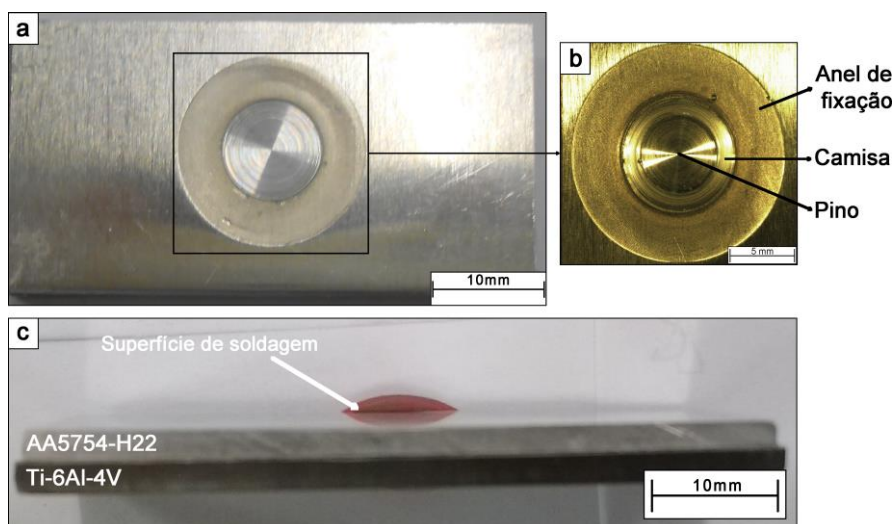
Junta AA5754-H22/Ti-6Al-4V como recebida: (a) topo da solda; (b) detalhe da região soldada; (c) imagem transversal da junta soldada.
